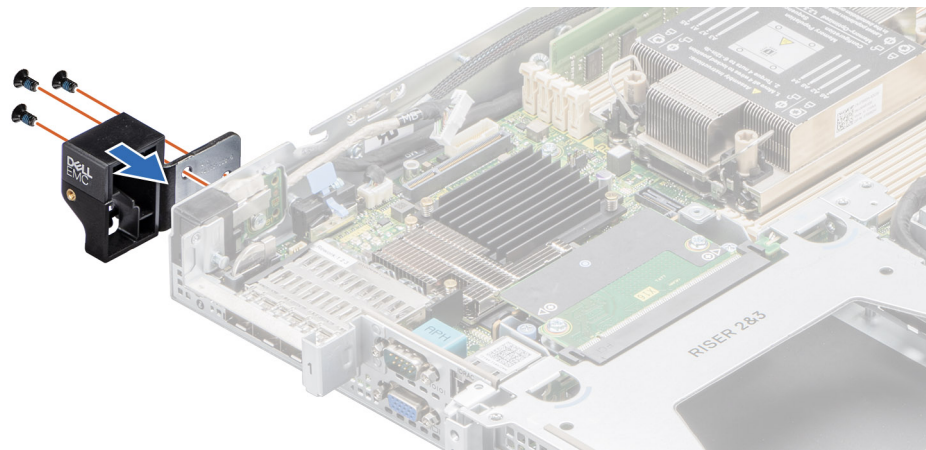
Instalación de la lengüeta izquierda para la configuración de acceso frontal
